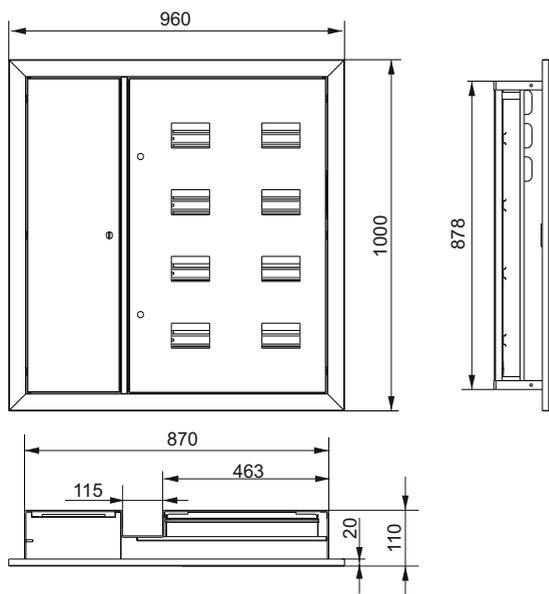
Корпус на 7 и 8 квартир (слаботочный отсек слева)
